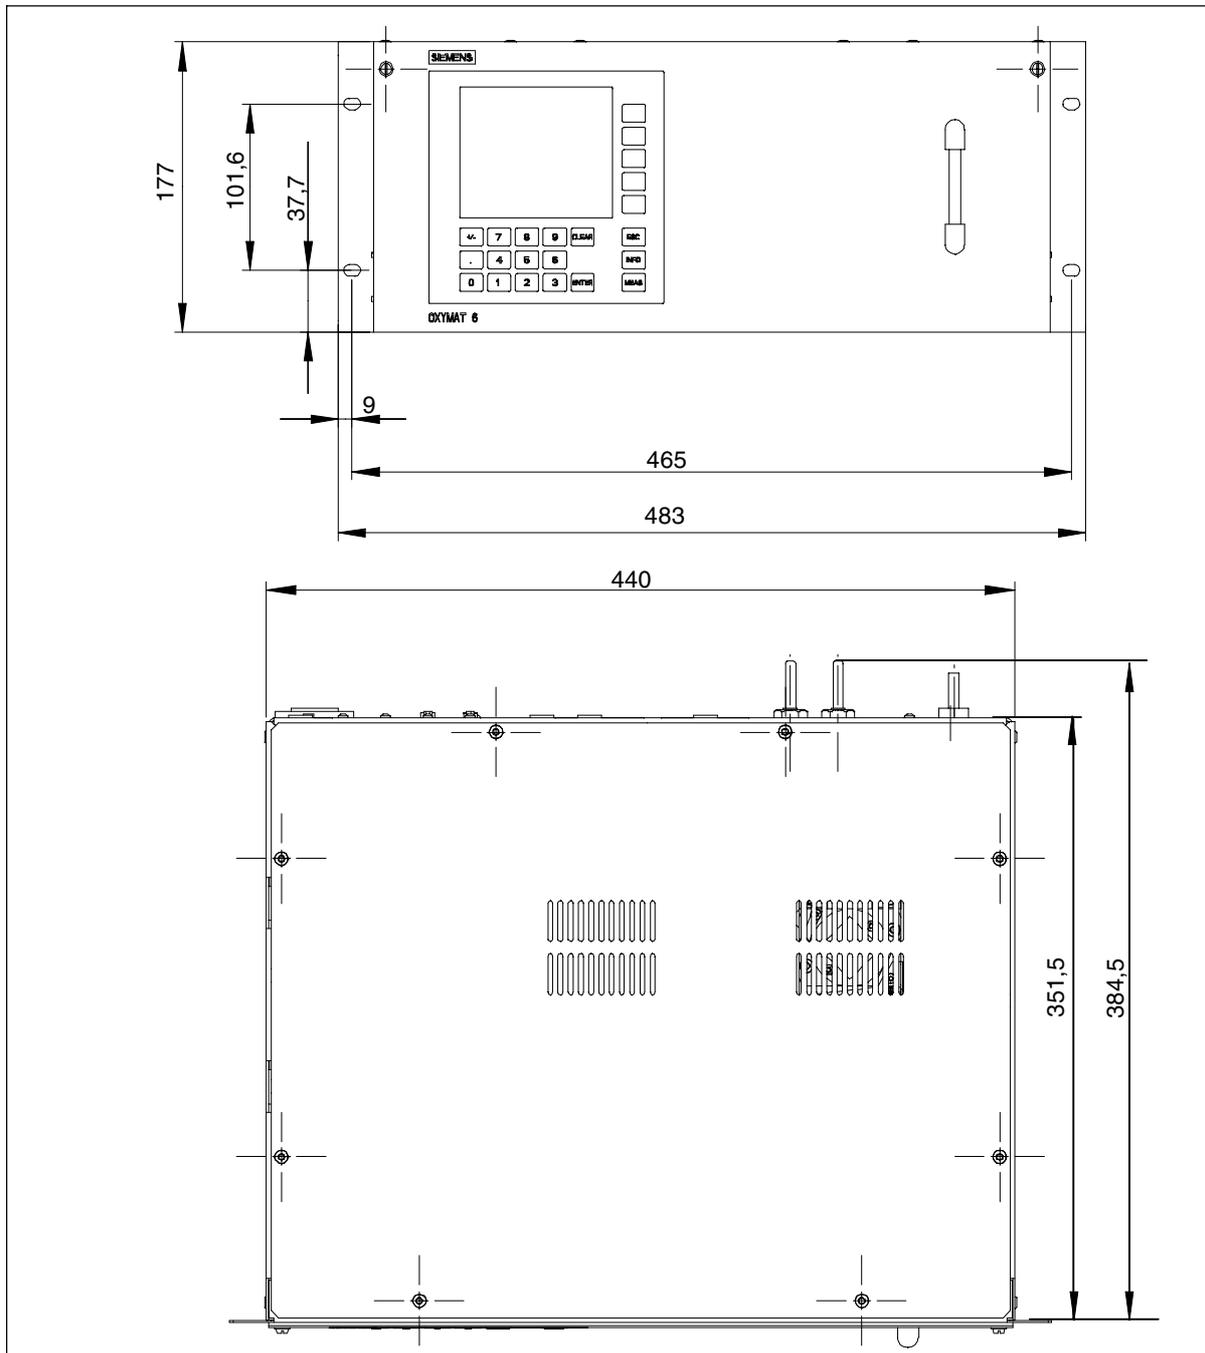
Maße zur Installationsvorbereitung (Vorderansicht und Draufsicht), gültig für BA 6000-O2 Einschub
